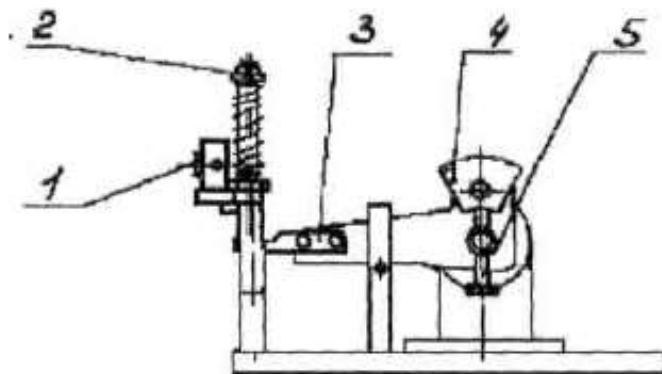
Тормоз для нагрузки стартера при полном торможении
